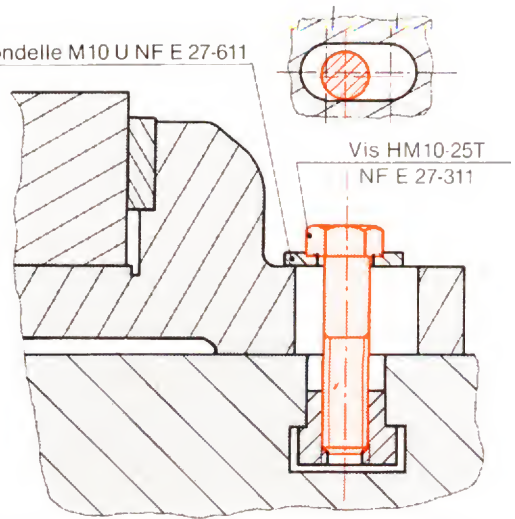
Montage par vis : etau de machine-outil.
